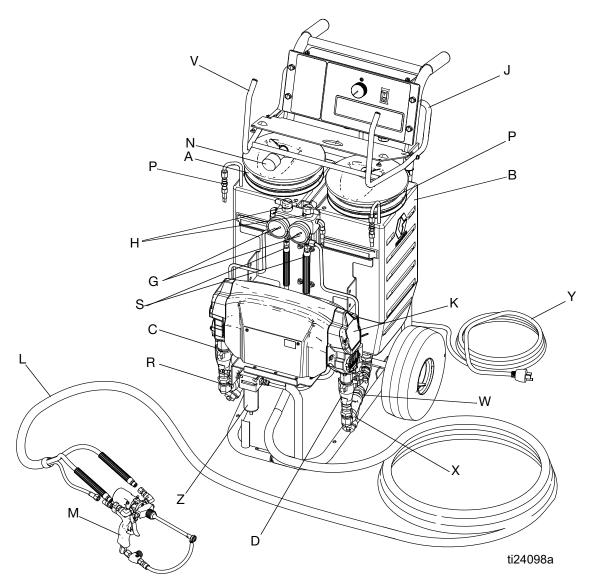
Identificación de los componentes, sistemas sin calentador (ref. pieza 249808 representada)
